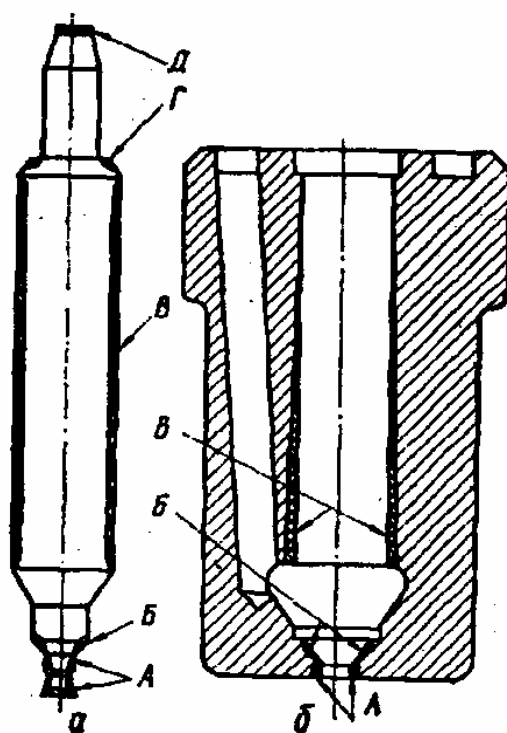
Місця і характер спрацювання деталей розпилювача штифтової форсунки: а – поверхонь голки: А – штифта; Б – запірного конуса; В – напрямної частини; Г – торцевої у спряженні з корпусом форсунки; Д – торцевої у спряженні із стержнем пружини; б – поверхонь корпуса розпилювача: А – сопла; Б – запірного конуса; В – напрямної частини
